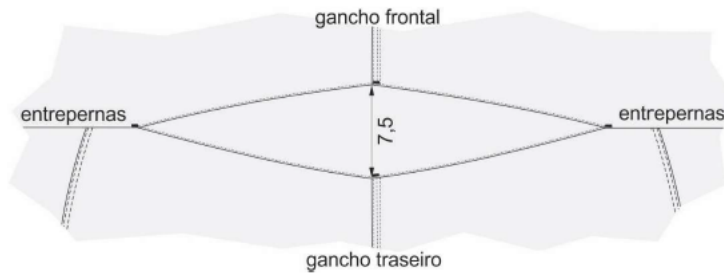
Recorte entre os ganchos frontal e traseiro (Medidas em cm)
